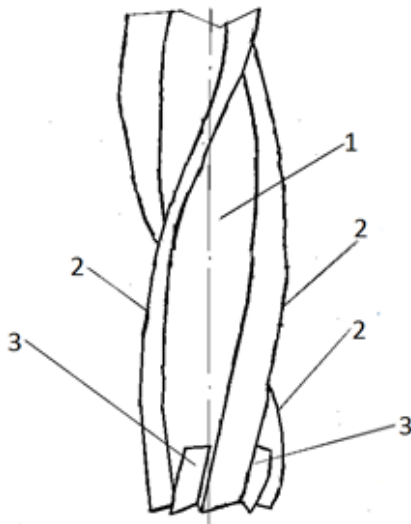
Длиннокромочная концевая фреза с дополнительно установленными зубьями в тоцовой части: 1 – корпус фрезы; 2 – зубья основной части фрезы; 3 – дополнительно установленные специальные зубья в торцевой части
